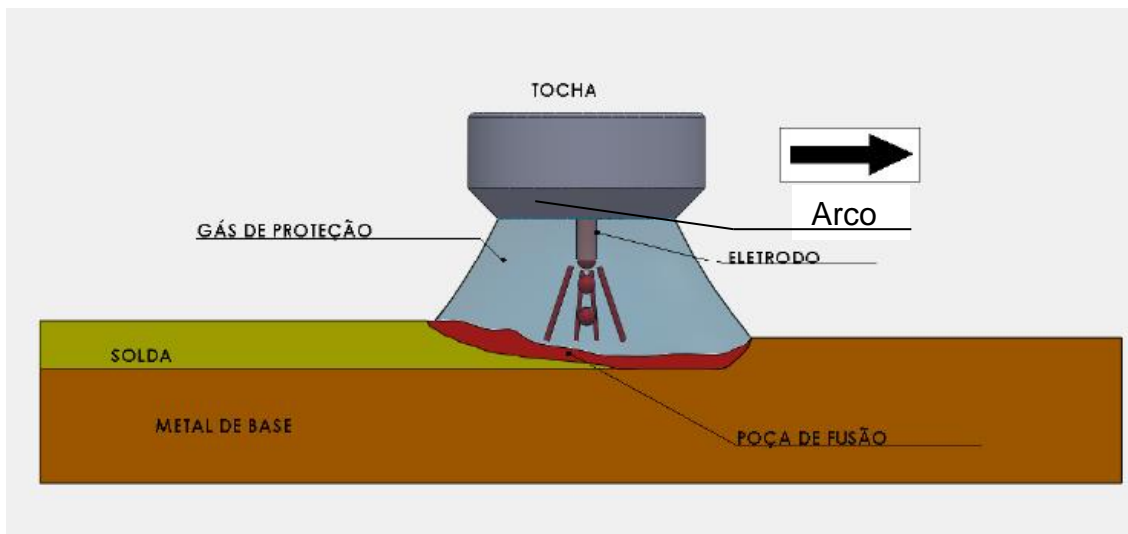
Configuração típica de um sistema de soldagem GMAW semi-automatizado.
